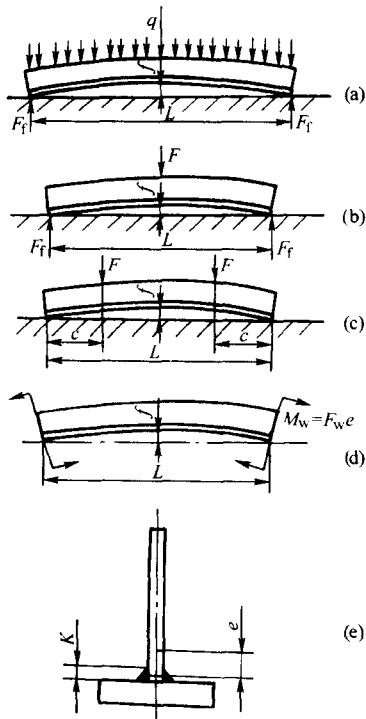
焊接 T 形梁的纵向变曲
